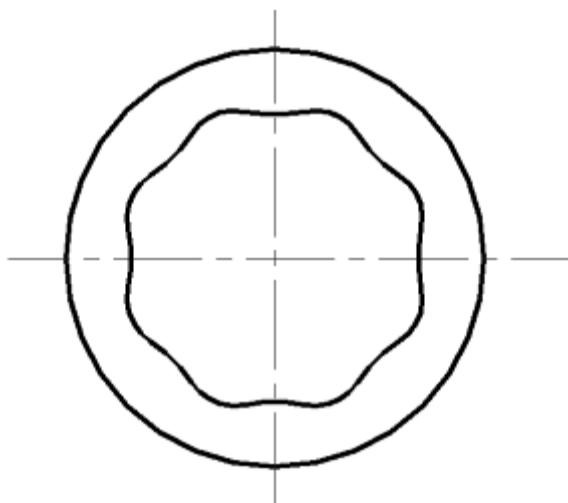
Форма внутренней поверхности трубы после редуцирования на стане с двухвалковыми рабочими клетями.
